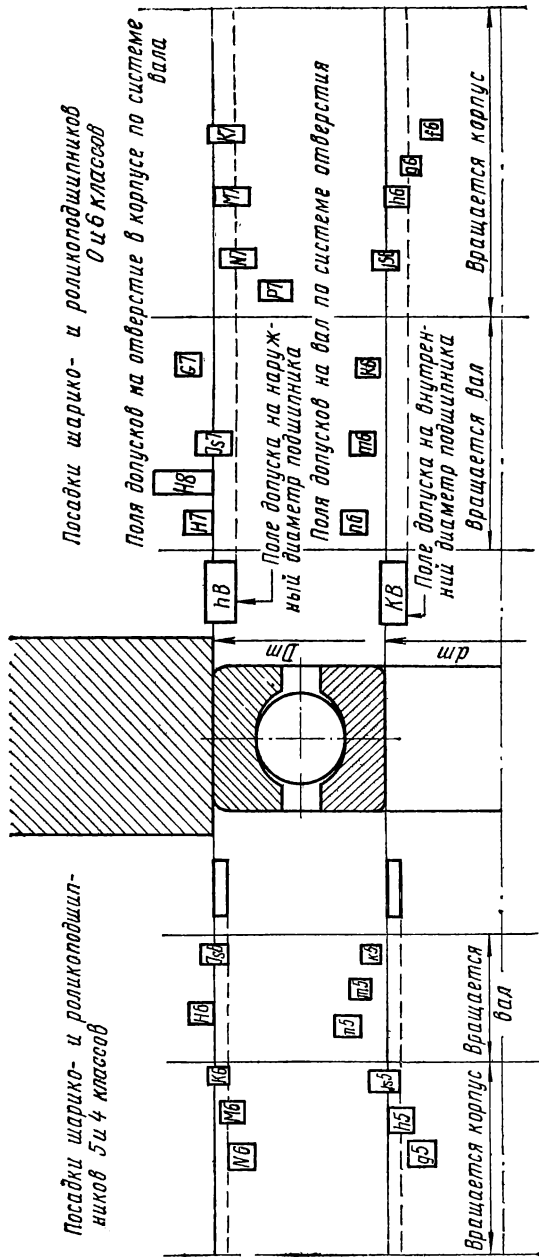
Посадки по присоединительным размерам шарикоподшипников
